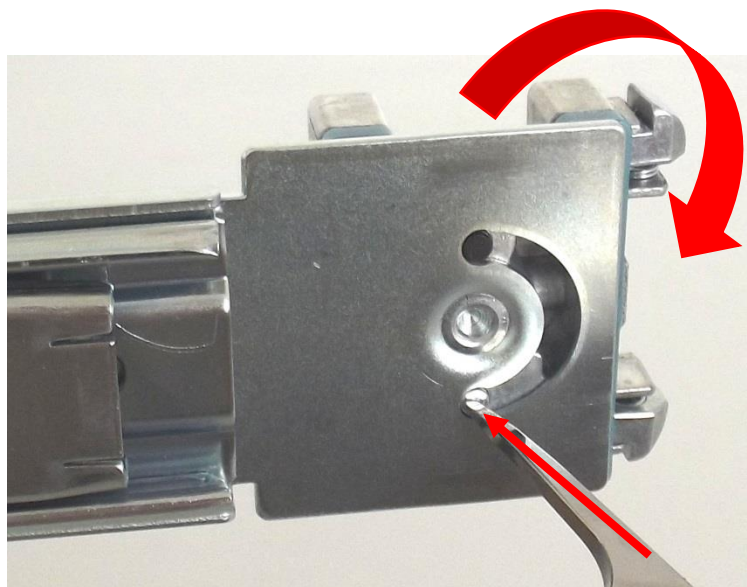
Drücken des Bolzens auf der Innenseite der Halterung
